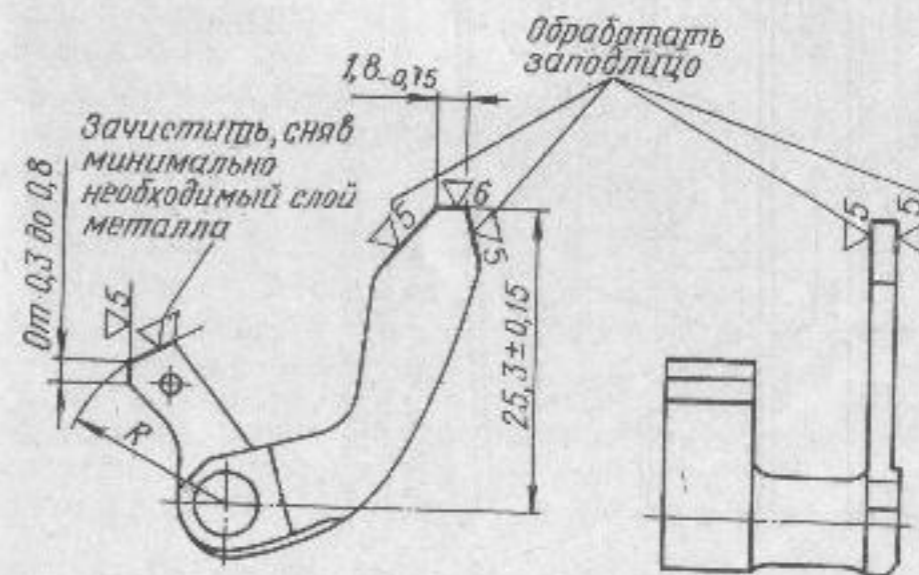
Зачистка шептала автоспуска и обработка после наплавки конца рычага автоспуска
